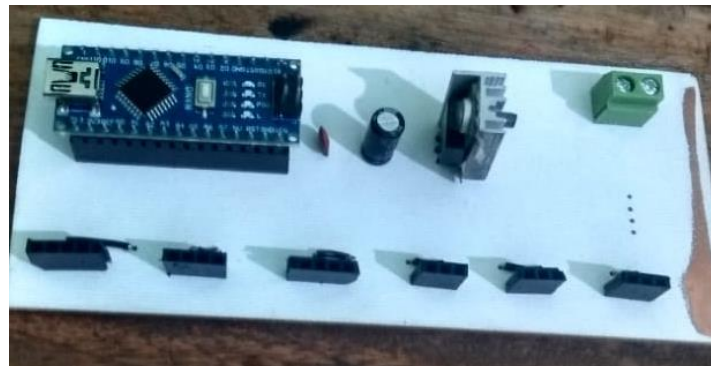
Vista superior de la PCB con el ensamble de arduino, su regulador de voltaje y pines de conexión de los sensores
